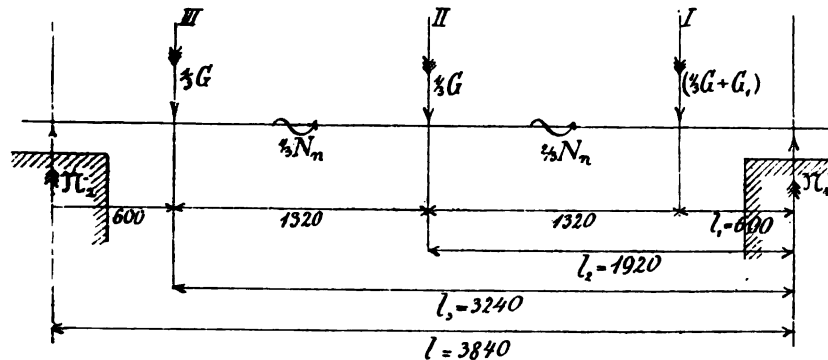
Kräfteplan zur Dimensionierung der Wasserradwelle.
